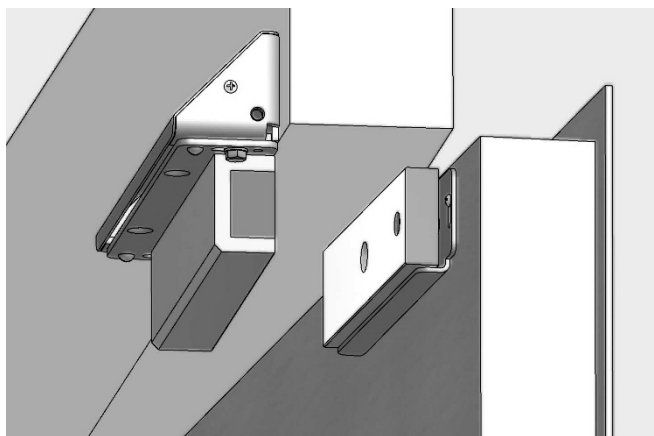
Установка корпуса замка с комплектом МК AL-350FB
